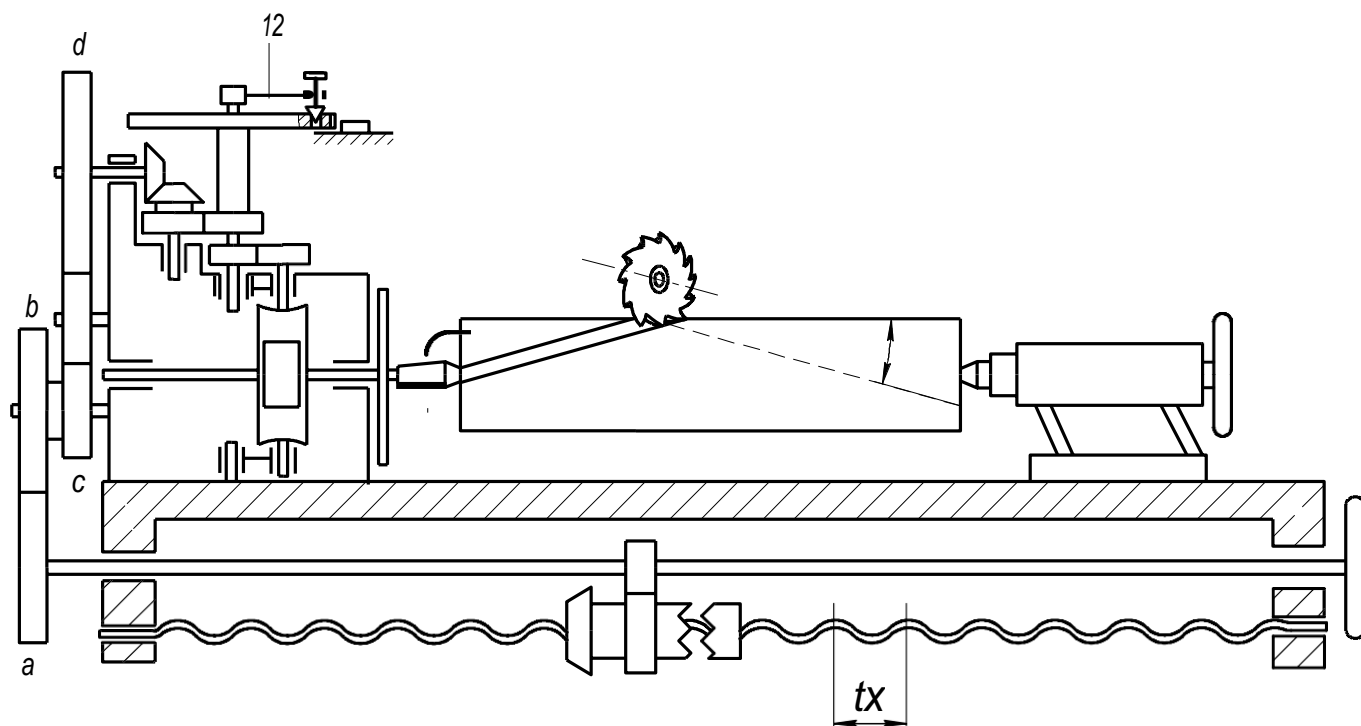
Кинематическая схема головки при нарезании винтовой канавки
